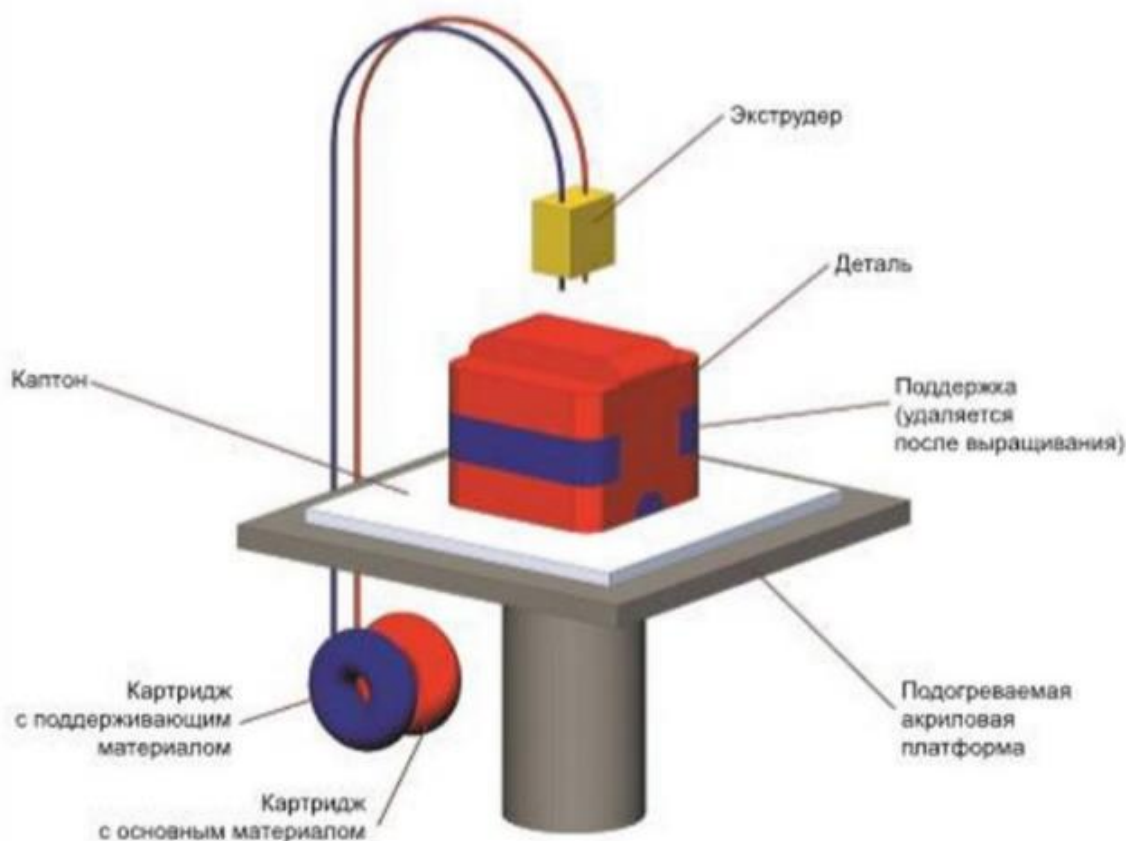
Схематическая зарисовка процесса печати по технологии послойного наплавления (FDM)
